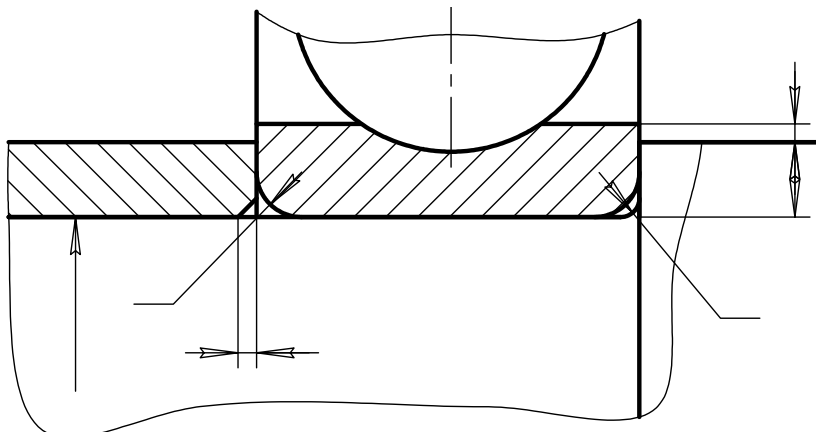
Уступ вала біля торця підшипника кочення
